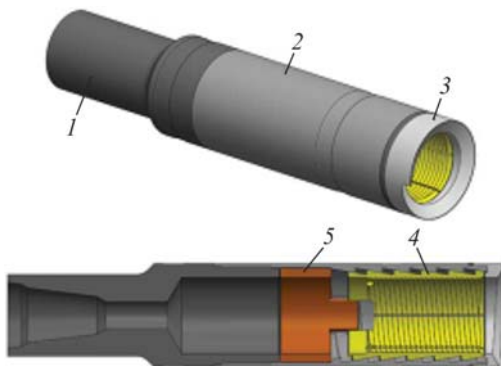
Общий вид труболовки наружной: 1 – переводник; 2 – корпус; 3 – воронка; 4 – цанга; 5 – кольцо направляющее
